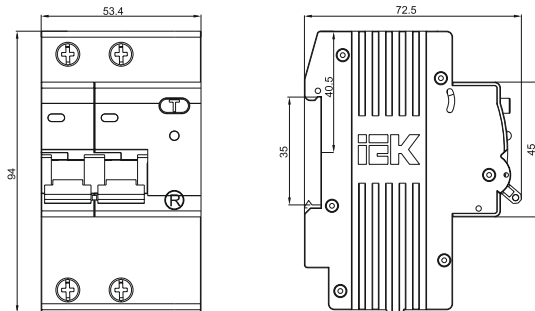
Габаритные размеры АД12М / Figure 2 – Overall dimensions of AD12M
